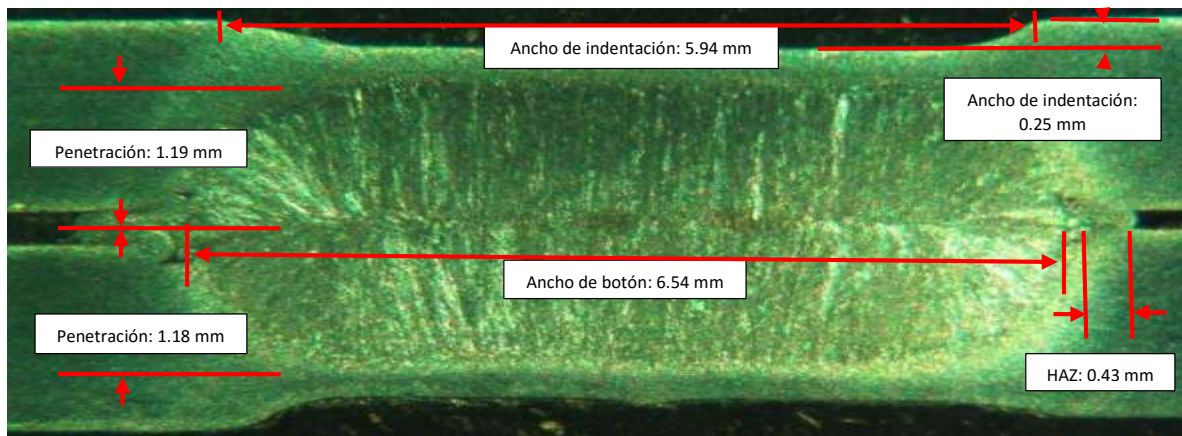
Mediciones realizadas en el botón de soldadura número 3.
